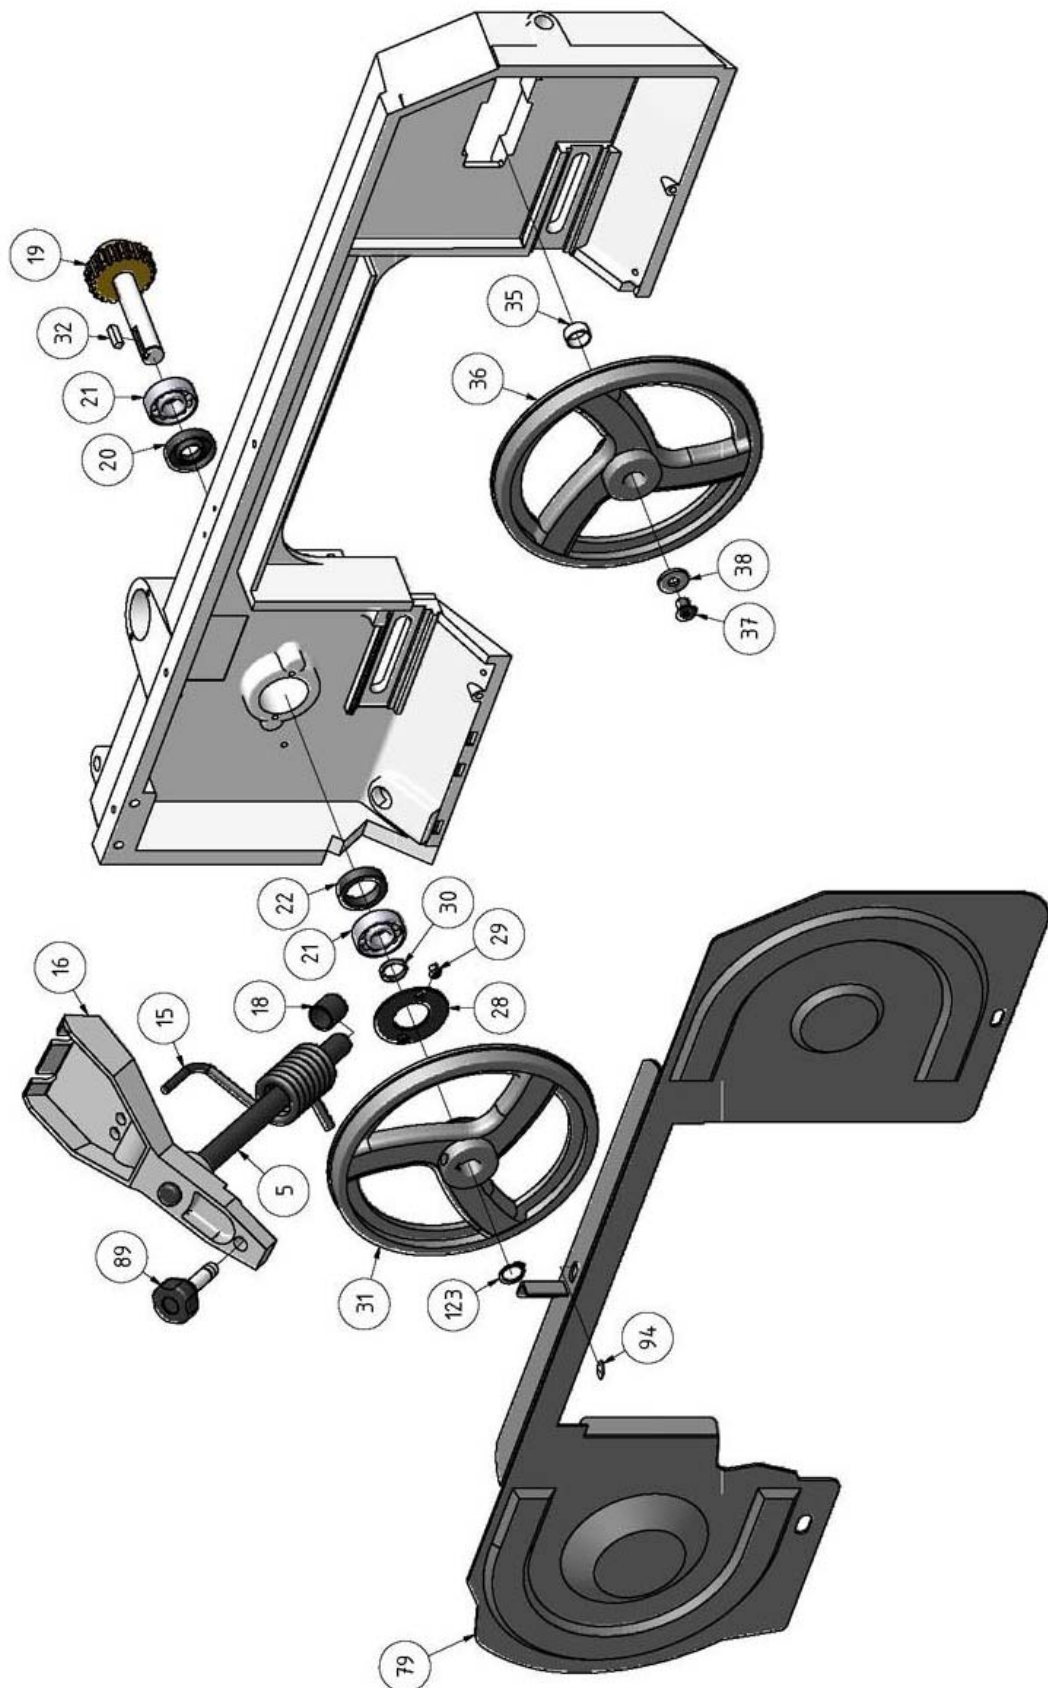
Ersatzteilzeichnung 2 von 4 - Parts drawing 2 of 4
